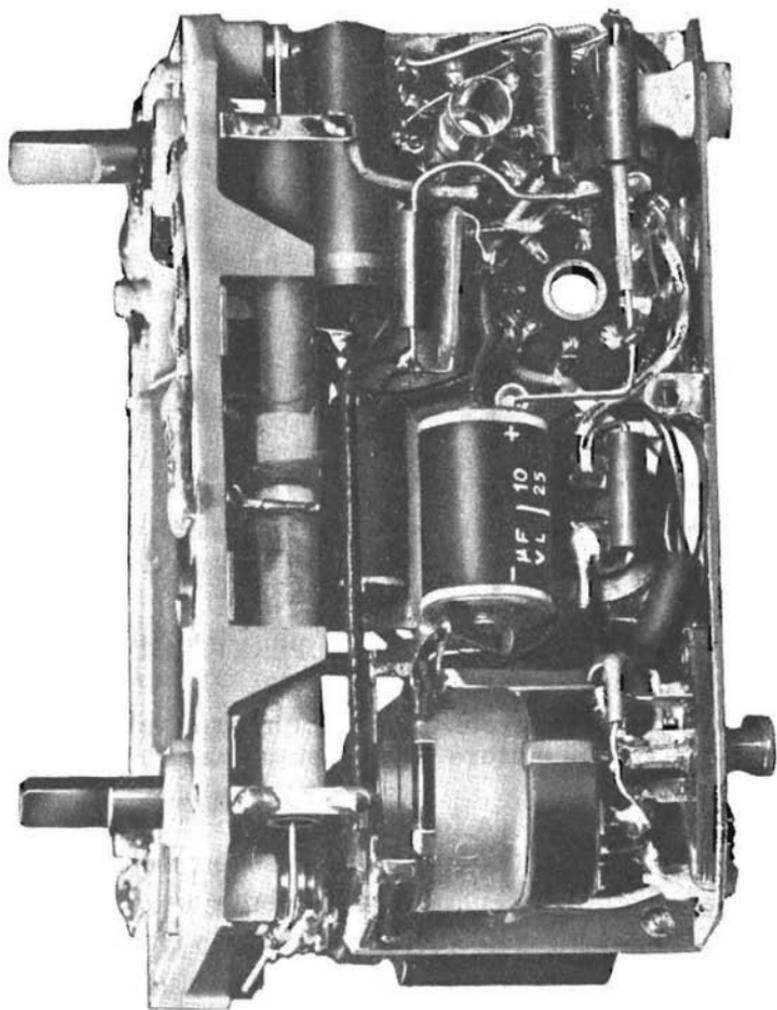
Aspetto finito del cablaggio. Si noti l'estrema compattezza.
